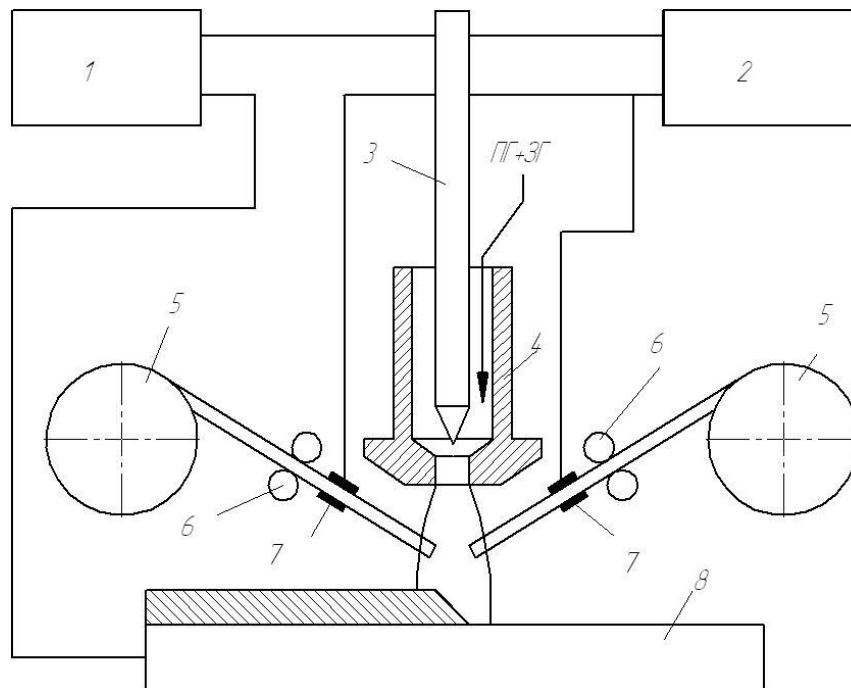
Схема плазменной наплавки двумя присадочными проволоками
